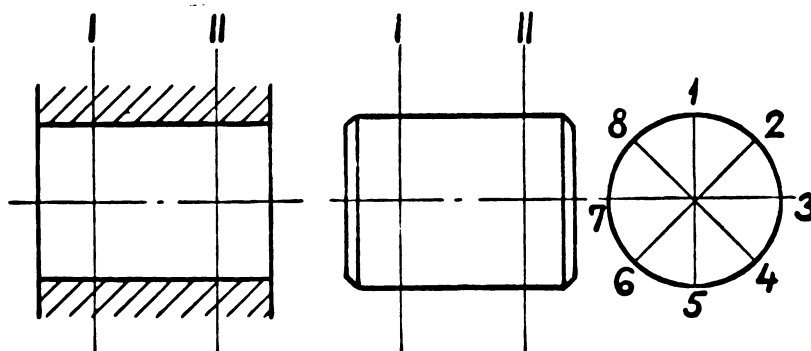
Schema de măsurare dimensională a probelor [56].
